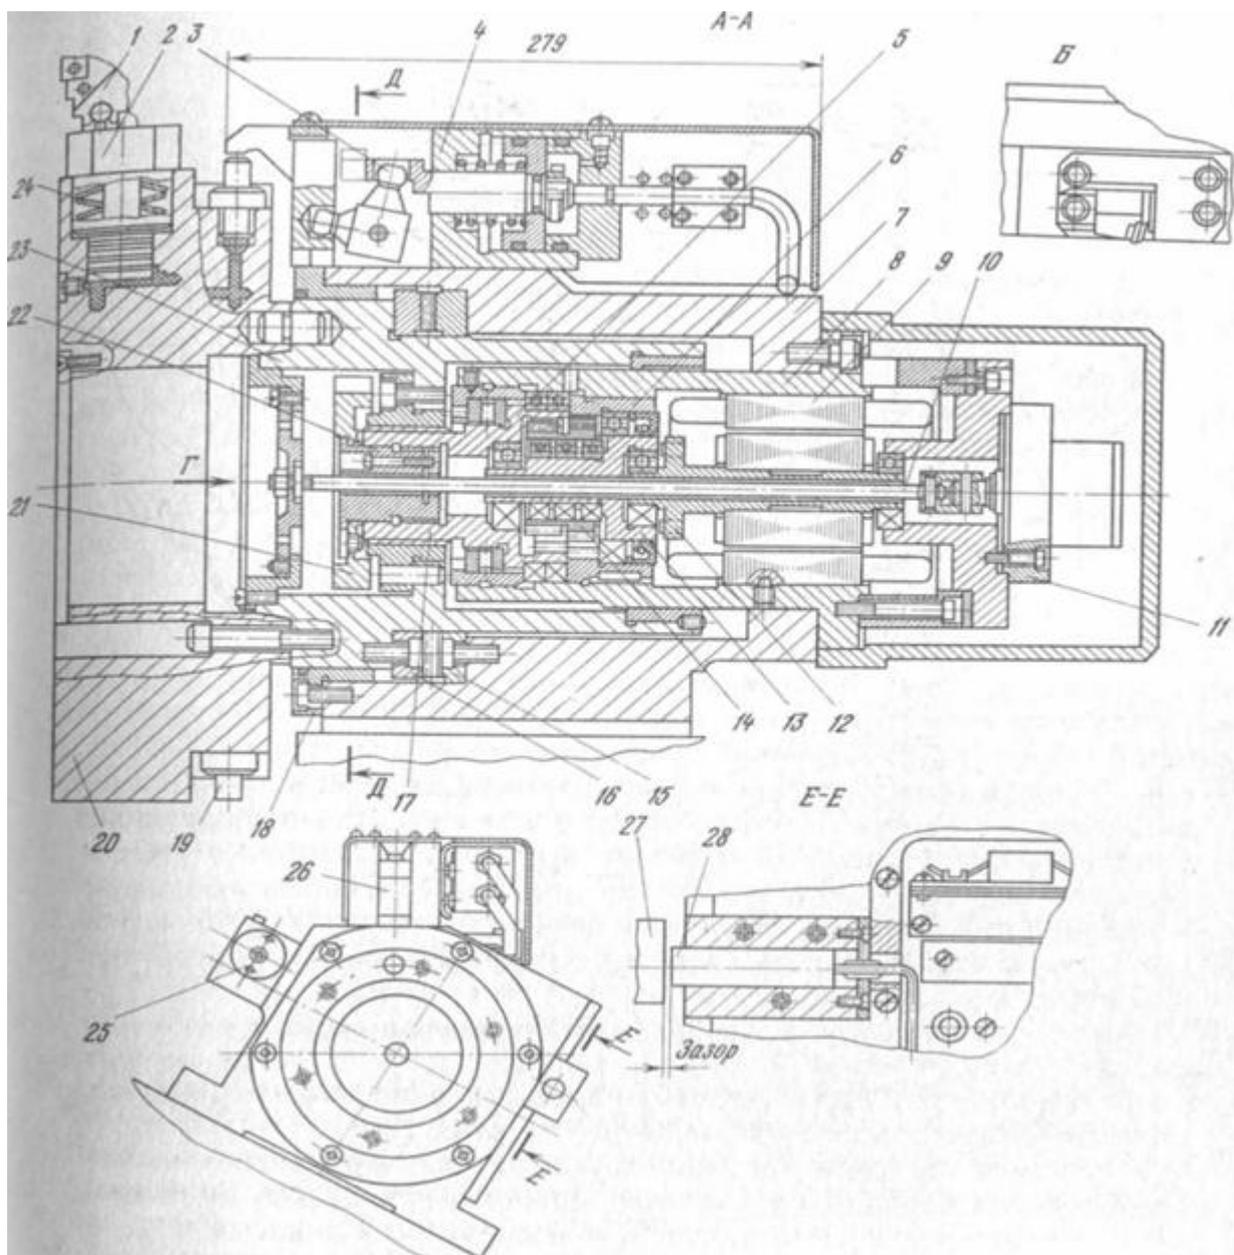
Револьверная головка с автоматической сменой инструмента.
